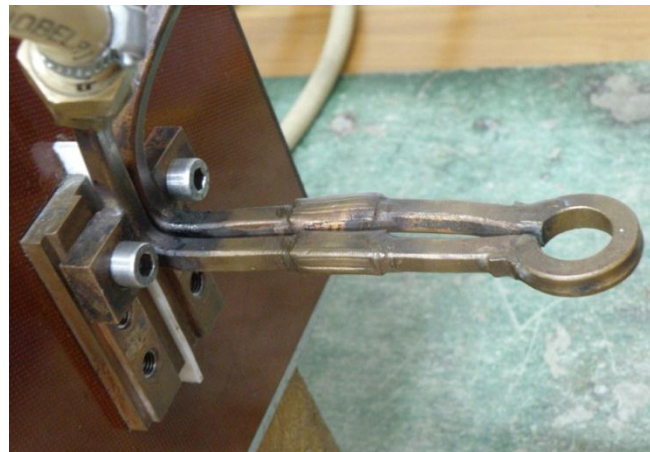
Detaliu cu inductorul utilizat la brazarea prin inducție
